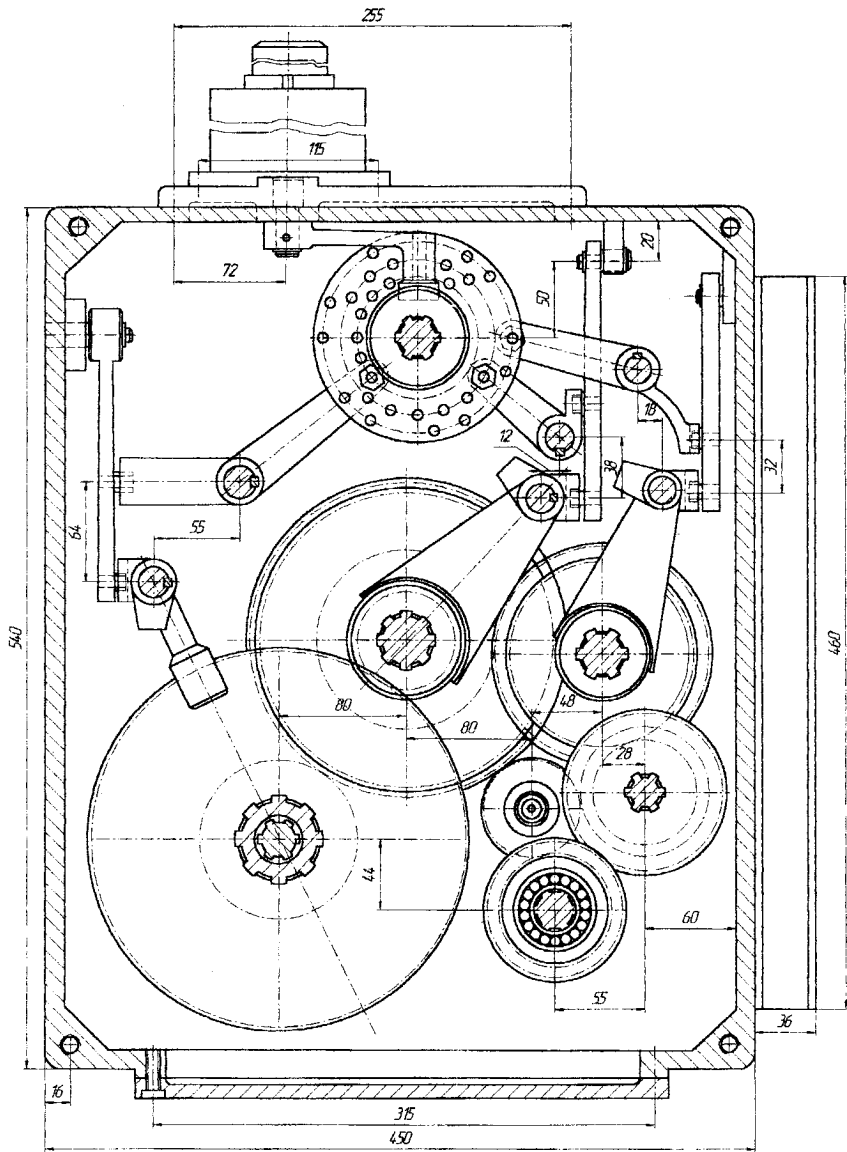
Коробка швидкостей фрезерного верстака з механізмом перемикання
